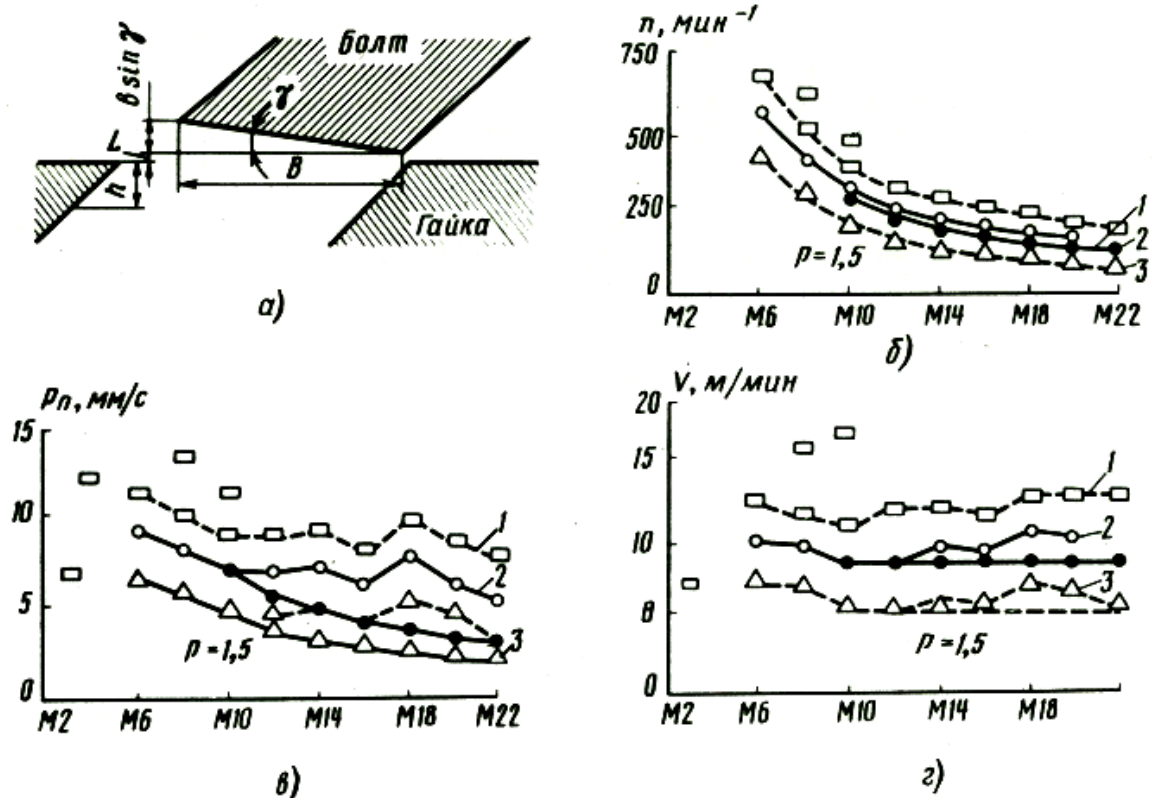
Схема соединения резьбовых деталей (а) и графики режимов сборочного процесса завинчивания винтов, болтов и шпилек с крупным шагом (б—г): 1—для посадки G/d; 2— для посадки G/e; 3— для посадки G/g; штриховыми линиями показаны значения для резьбы с мелким шагом
